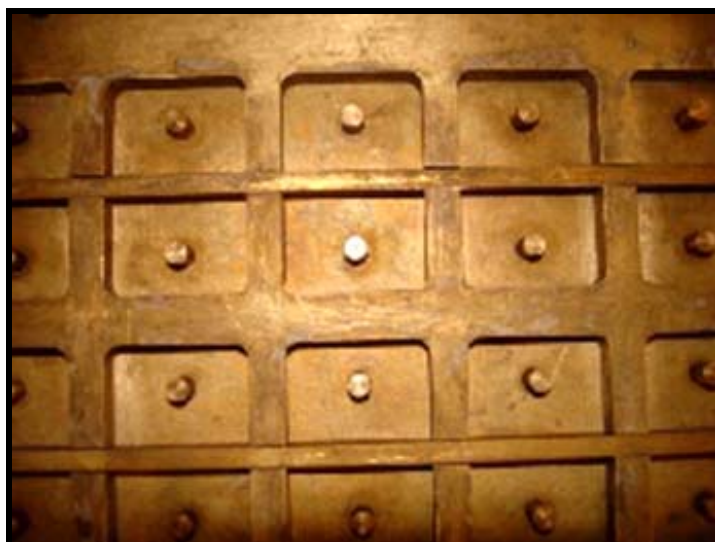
Posicionamento da placa central sobre a placa inferior da mufla com as barras espaçadoras metálicas em posição.
